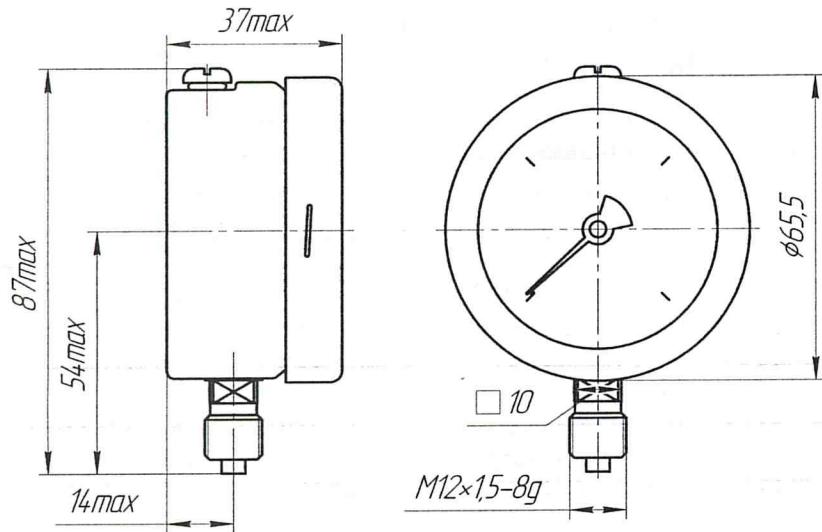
Габаритные и присоединительные размеры приборов с радиальным расположением штуцера без фланца
